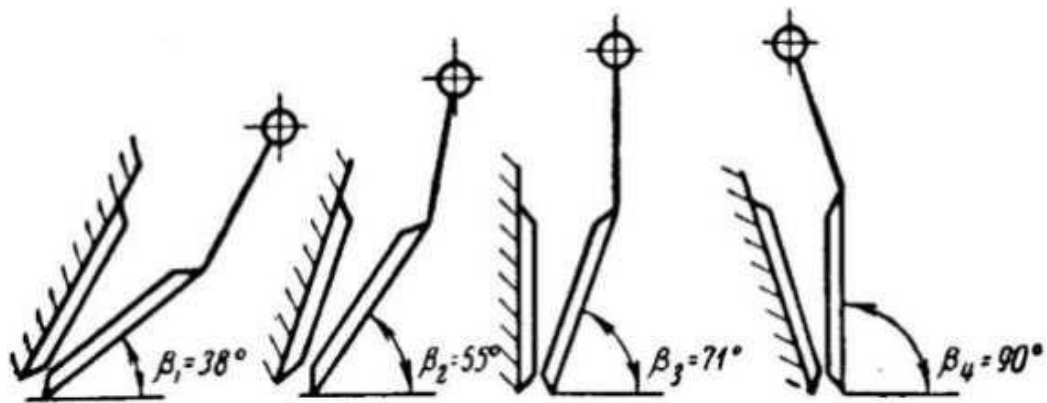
Варіанти розташування камери подрібнення щоквої дробарки [18]
